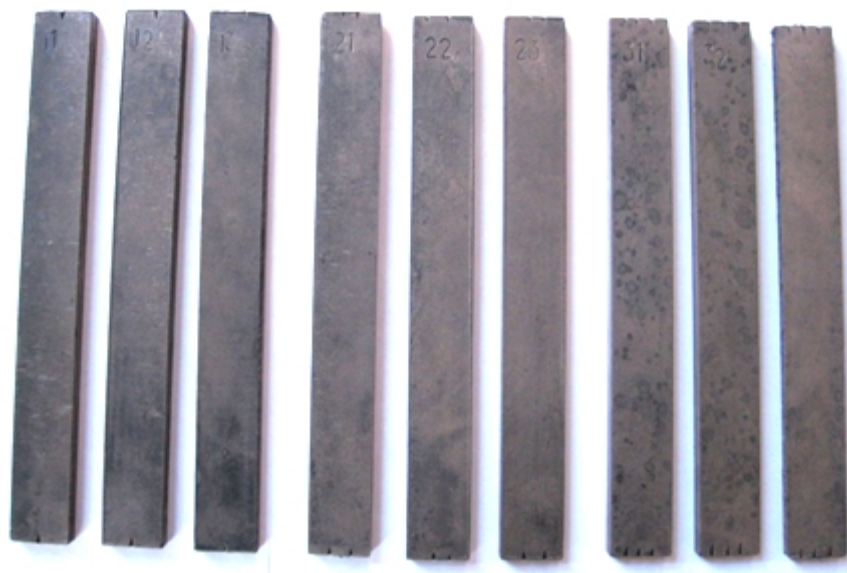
Пластины струмоприймачів електровозів, виготовлені методом порошкової металургії (загальний вигляд).
